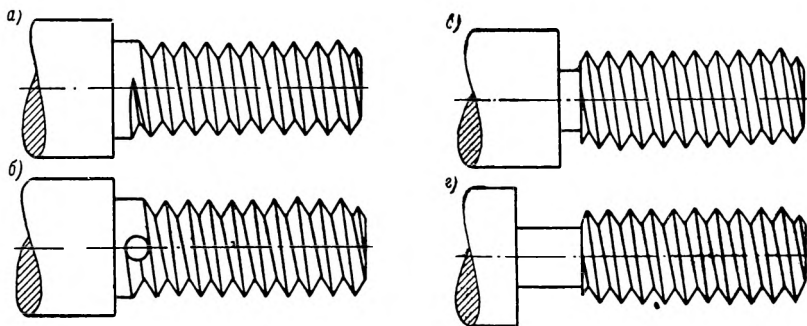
Конструкции схода резьбы по окончании нарезки.
